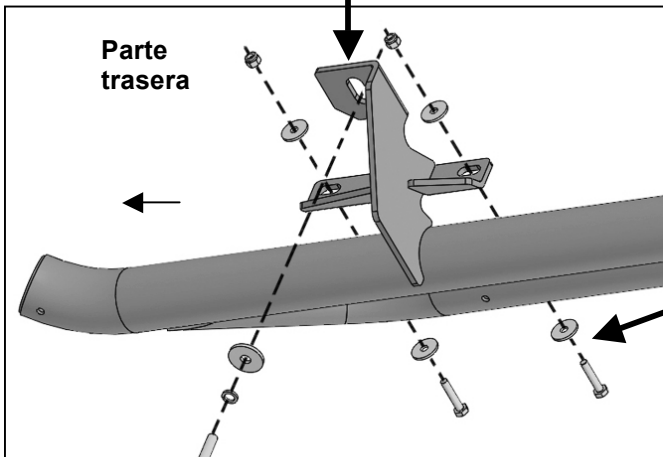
Soporte soldado delantero del lado izquierdo/del conductor fijado al área de soldadura de pellizco y al panel interior del piso
